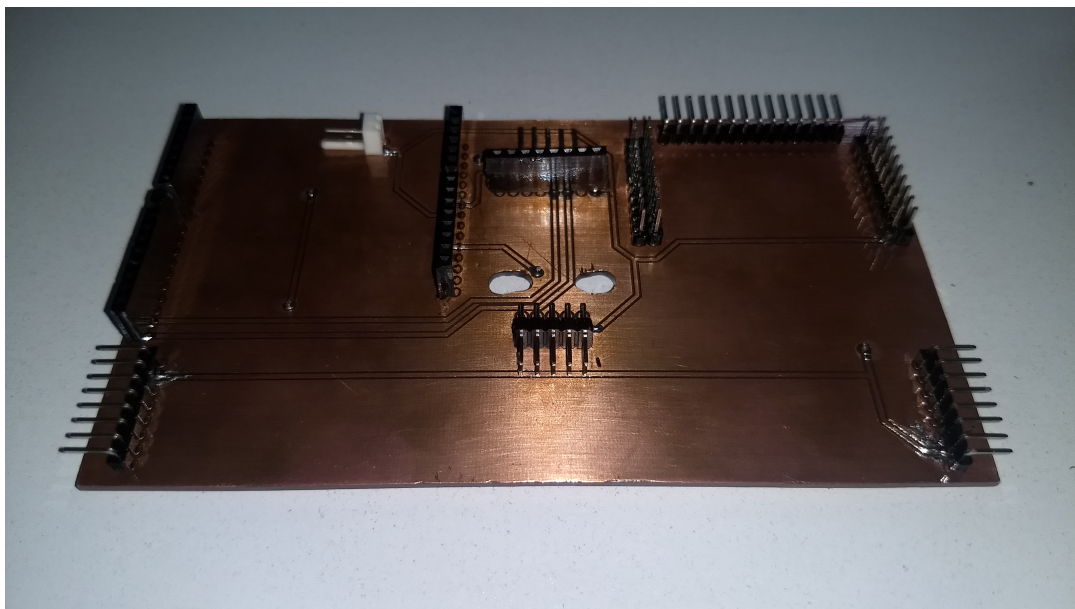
Soldado y acabado del circuito impreso, parte top
